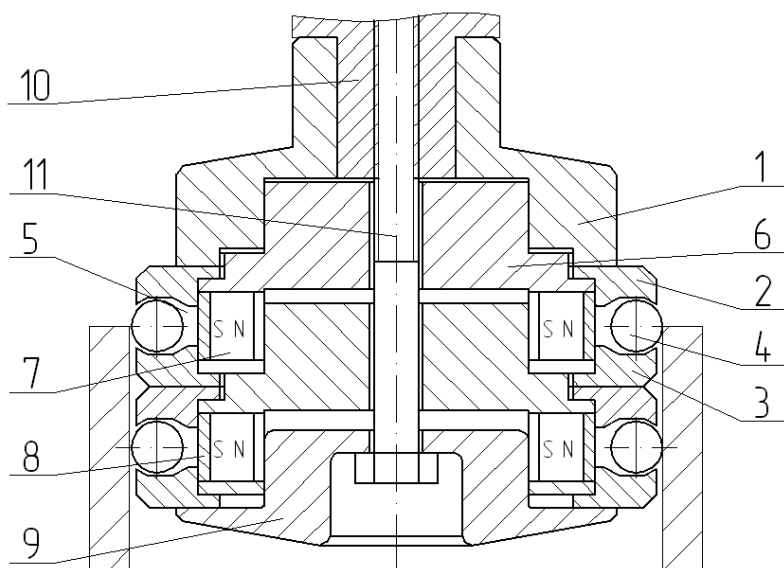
Схема способа магнитно-динамического упрочнения поверхности
